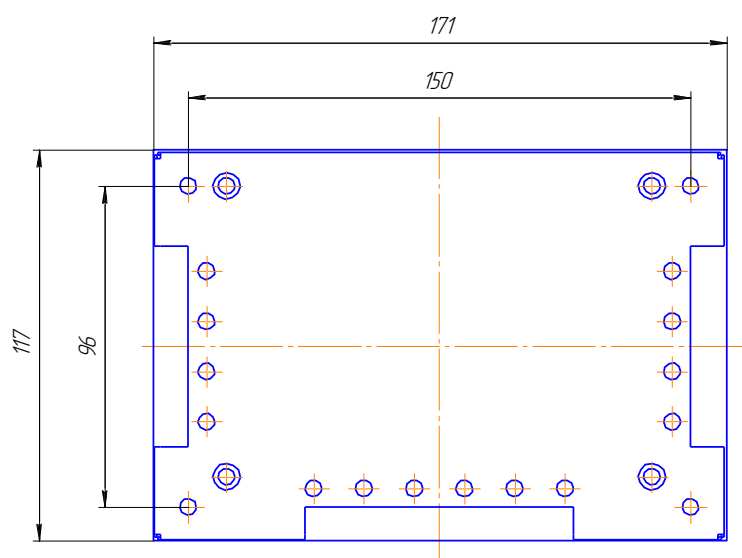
б. Разметка крепления АКС в металлическом корпусе.
